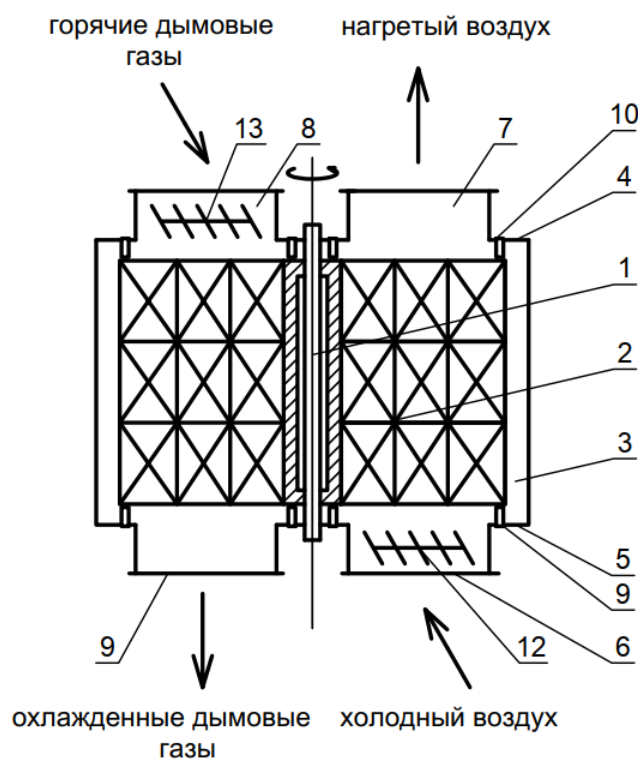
Самовращающийся регенеративный воздухоподогреватель
